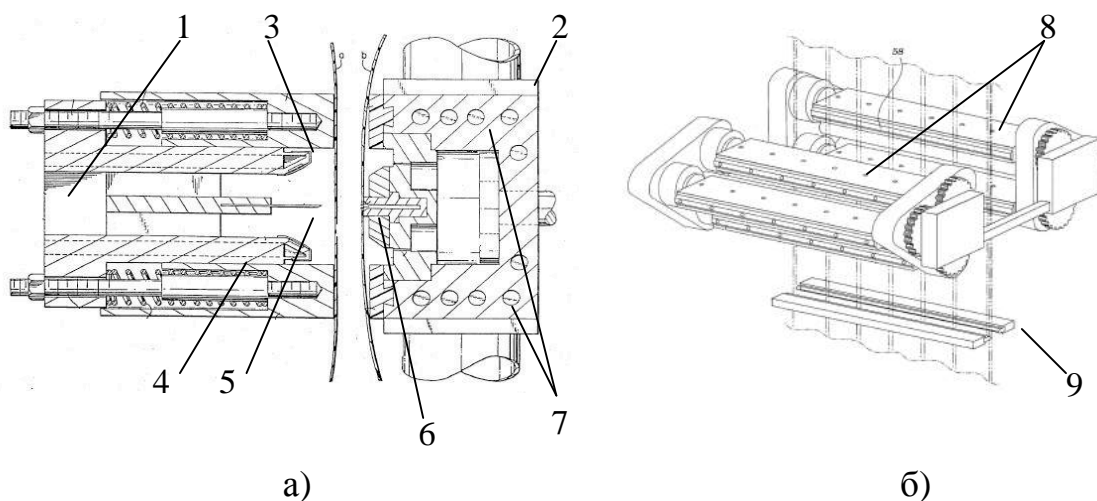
Механізми поперечного зварювання при безперервному русі плівки:
